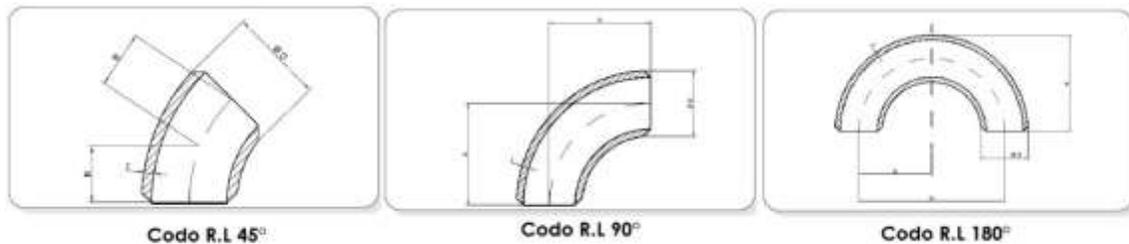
Tipos de codos de radio largo de 45°, 90° y 180°. Fuente: Catalogo Tubos y accesorios en acero al carbono soldado y sin soldadura Normas EN (DIN) y ASTM. Tubasol S.A
